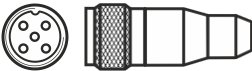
ZBE-- - Buchse 5-polig mit Schraubklemme
